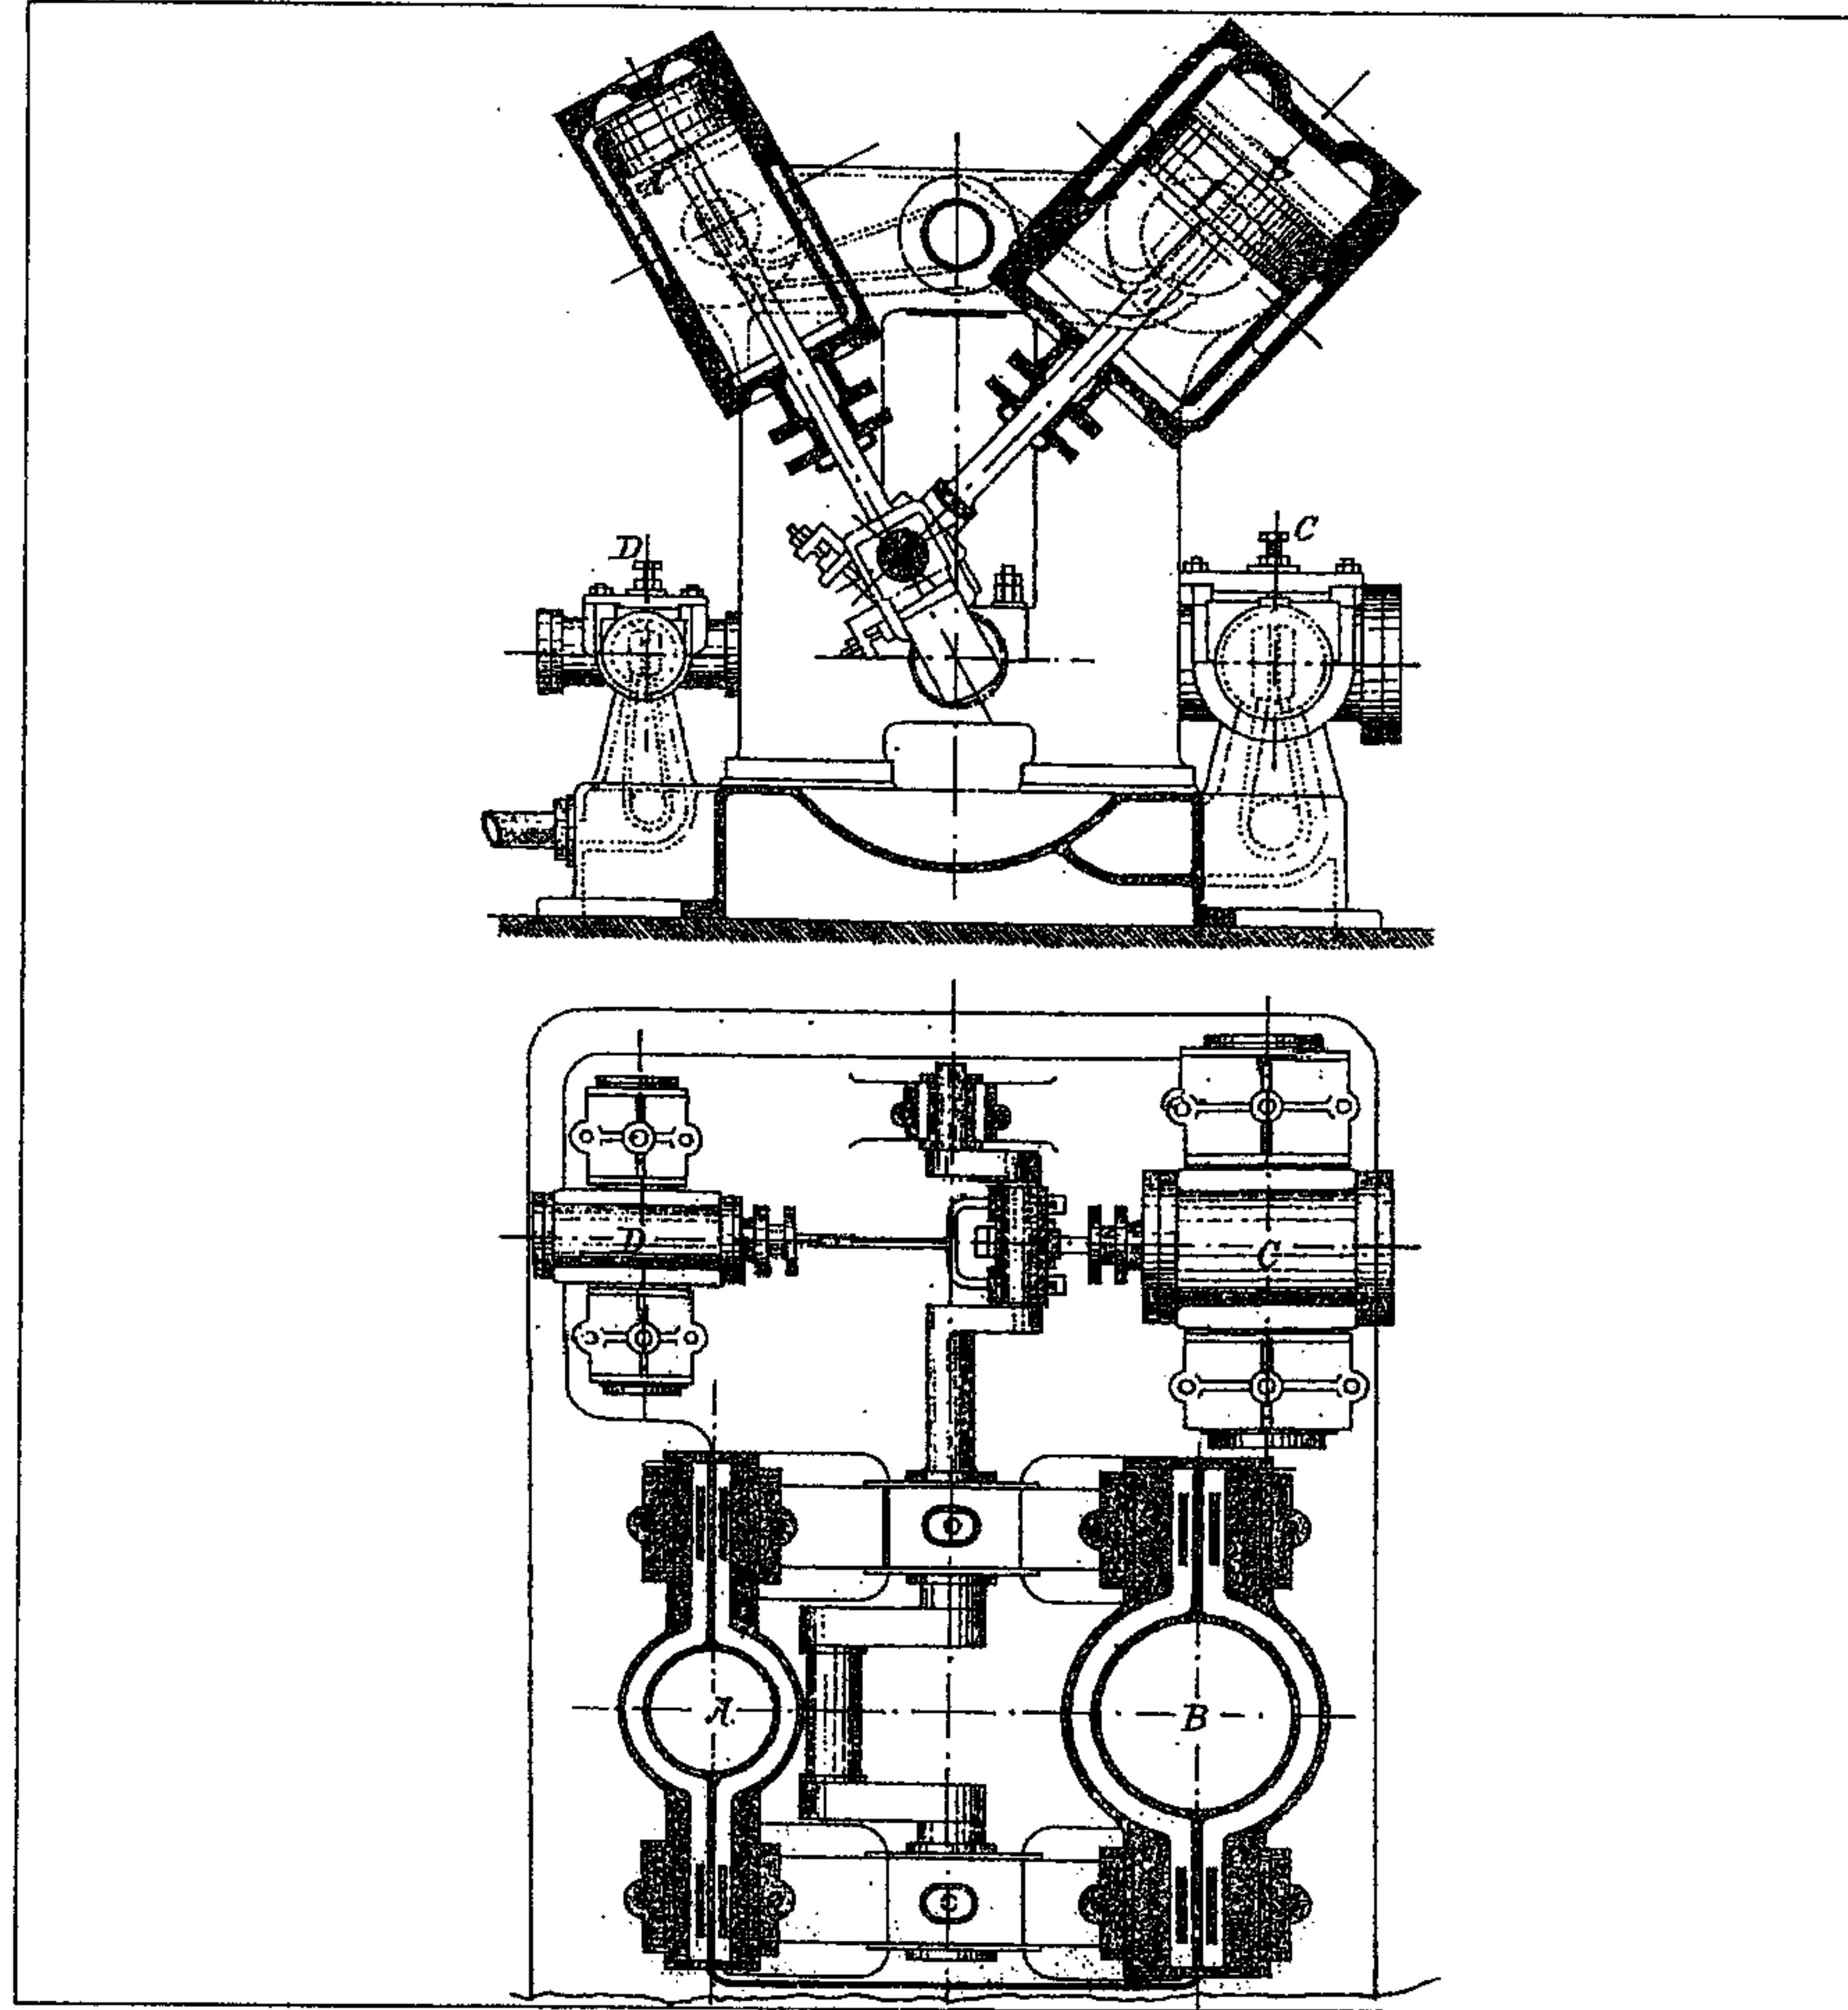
/4: Prinzipskizze einer oszillierenden Lokomobilmaschine mit vierfacher Expansion, Patent von Joh. Haag (um 1875)
